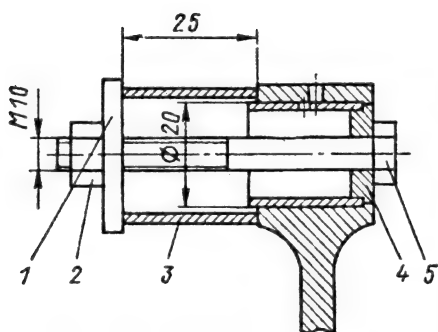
Приспособление для выпрессовки и запрессовки бронзовой втулки малой головки шатуна
